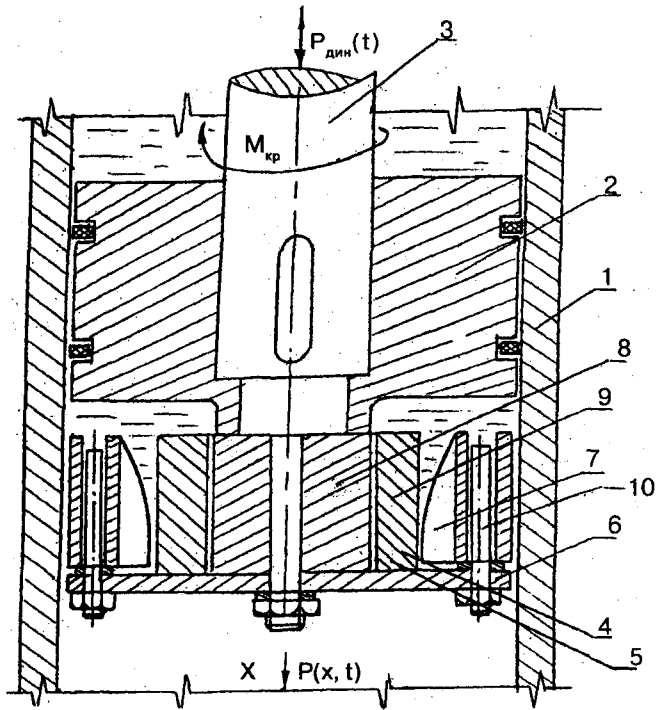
Принципиальная схема гидропульсатора комбинированного типа, с подвижными лопатками на рабочем колесе: 1 – корпус; 2 – поршень; 3 – шток; 4 – устройство для создания дополнительных колебаний; 5 – рабочее колесо; 6 – спицы; 7 – лопасти; 8 – кулачок; 9 – шатун; 10 – консольные оси
